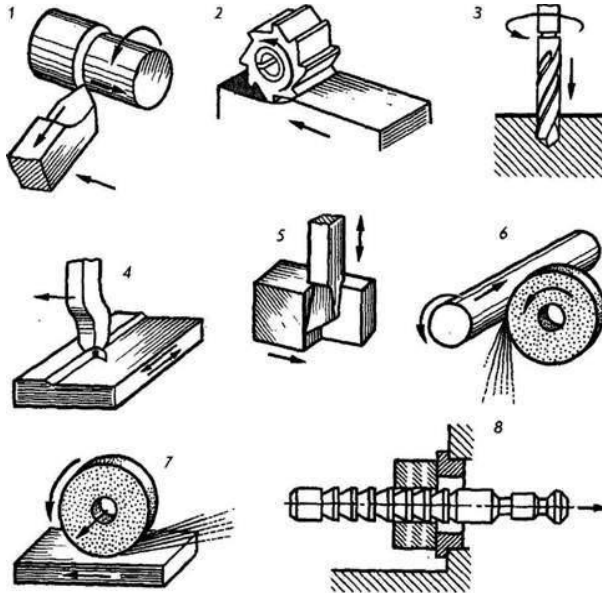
Найпоширеніші методи механічного оброблення в машинобудуванні: 1 – точіння; 2 – фрезерування; 3 – свердління; 4 – стругання; 5 – довбання; 6, 7 – шліфування; 8 – протягання
